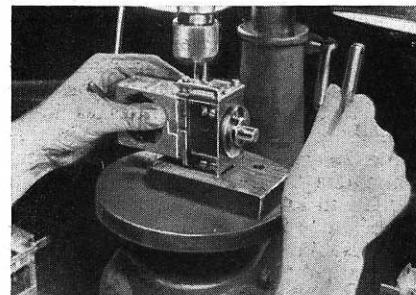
Bohren des gegossenen Innenteils der EXAKTA Varex.
